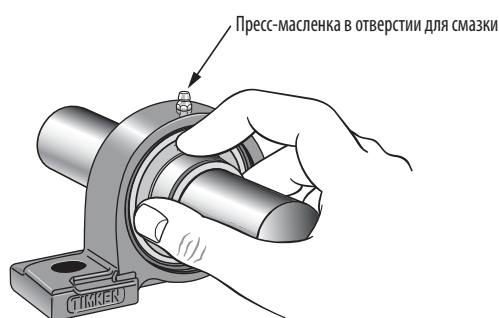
Установка пресс-масленки в резьбовое отверстие для смазки.
